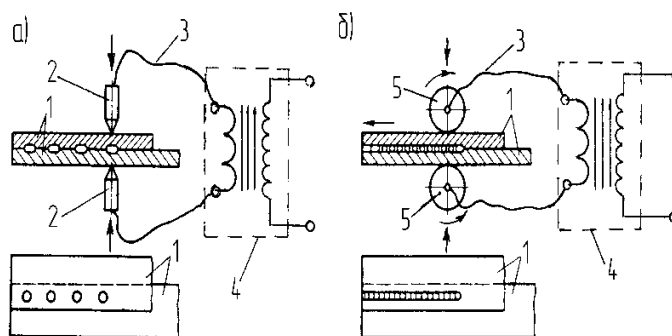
Схемы контактной сварки: а) - точечной; б) – шовной: 1 - свариваемые листы (детали); 2 - электроды; 3 - токопроводы; 4 - сварочный трансформатор; 5 - роликовые электроды
